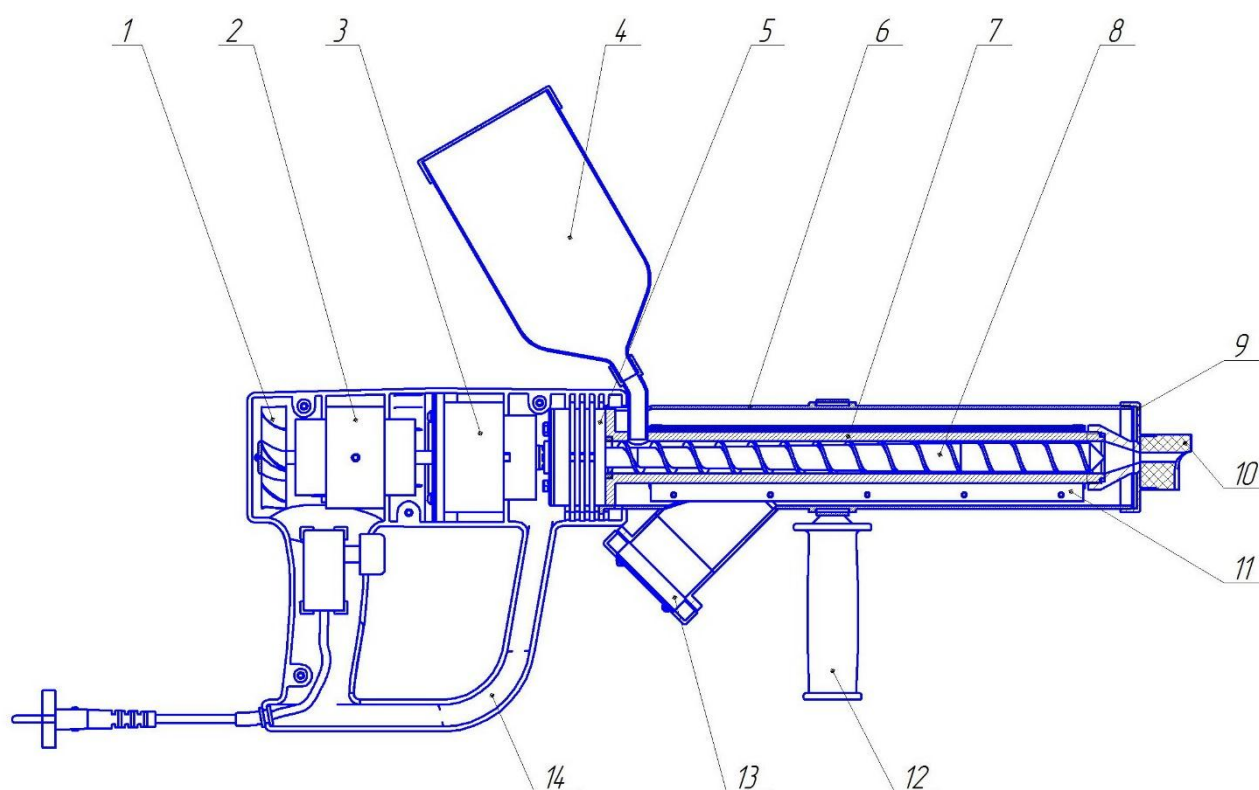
Схема ручного сварочного экструдера
